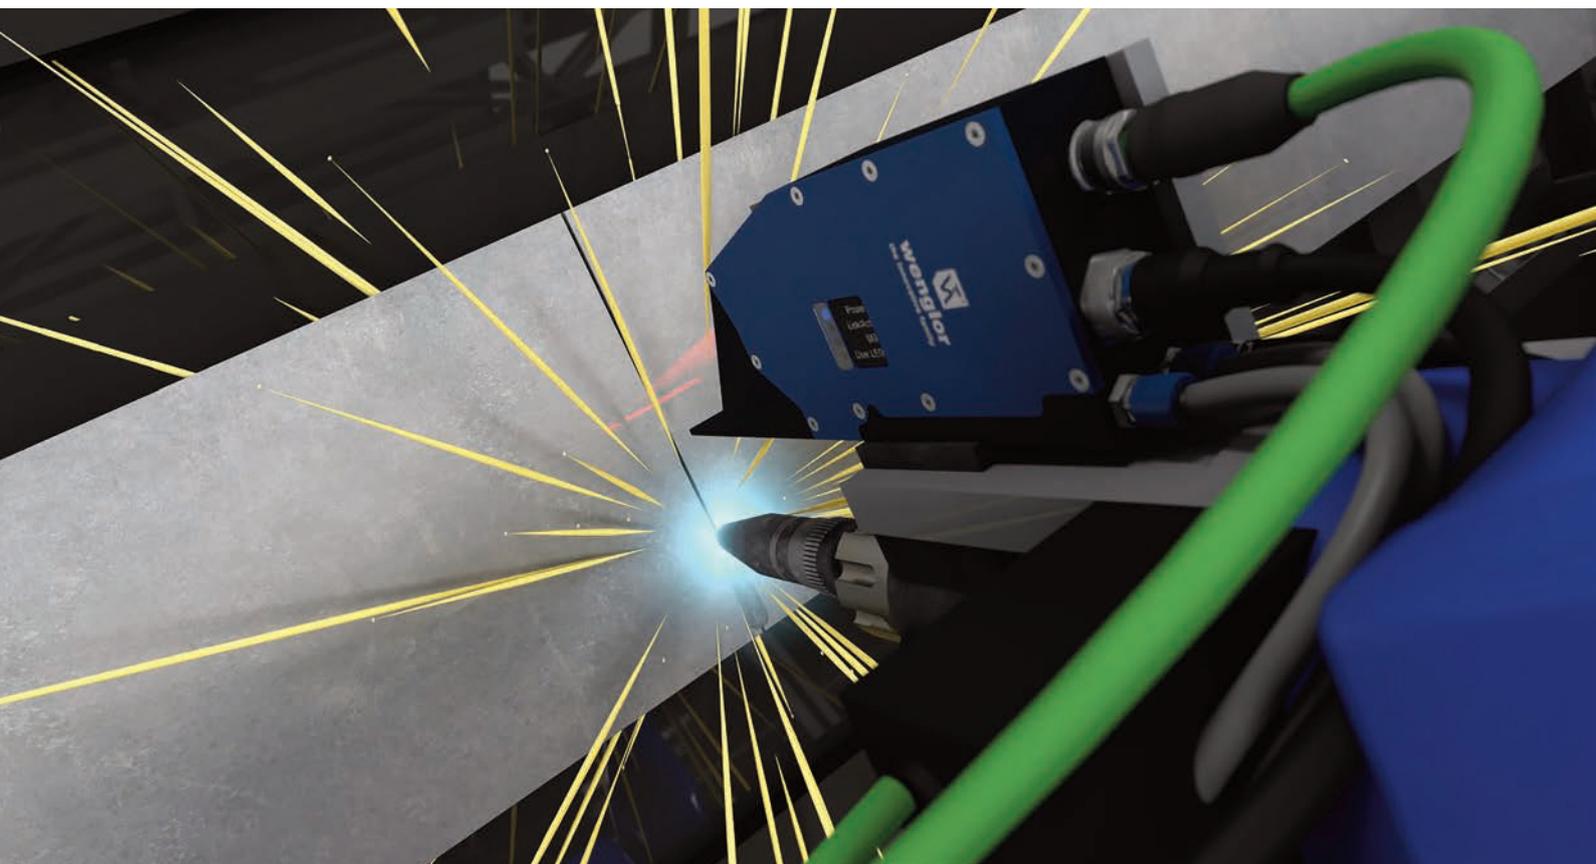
| Automatisierte Schweißnahtführung in Roboterschweißzellen mit dem 2D-/3D-Profilsensor weCat3D MLZL. Der Sensor benötigt weder ein zusätzliches Schutzgehäuse, noch muss er zur Ausrichtung gekippt werden.
